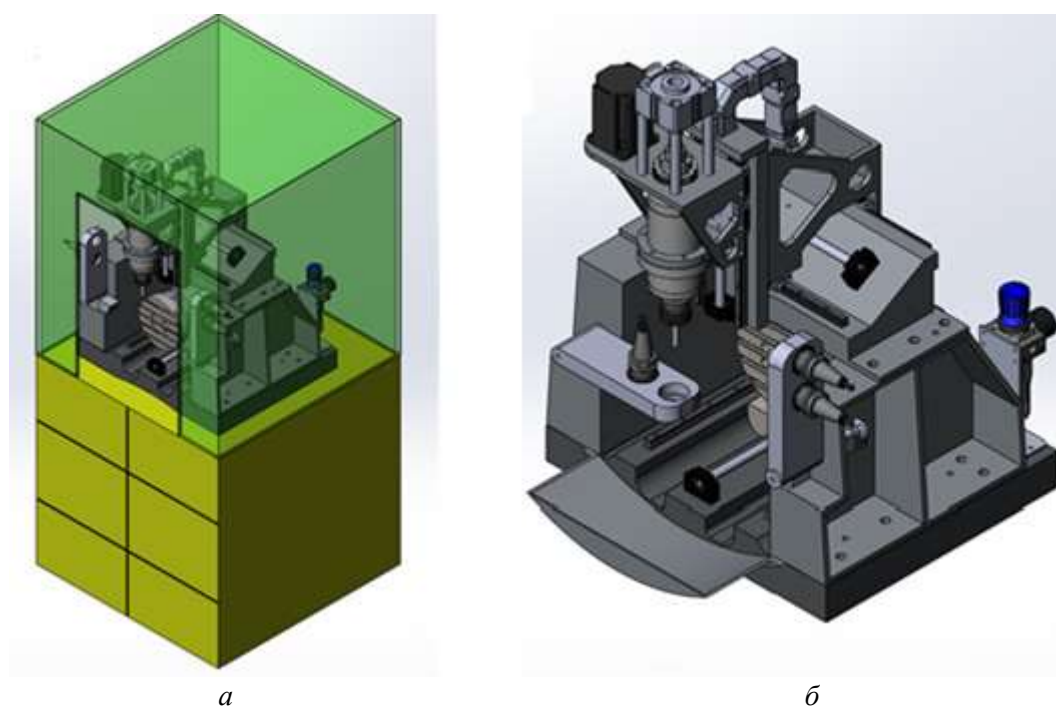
Малогабаритный 4-х осевой фрезерный станок с ЧПУ:
